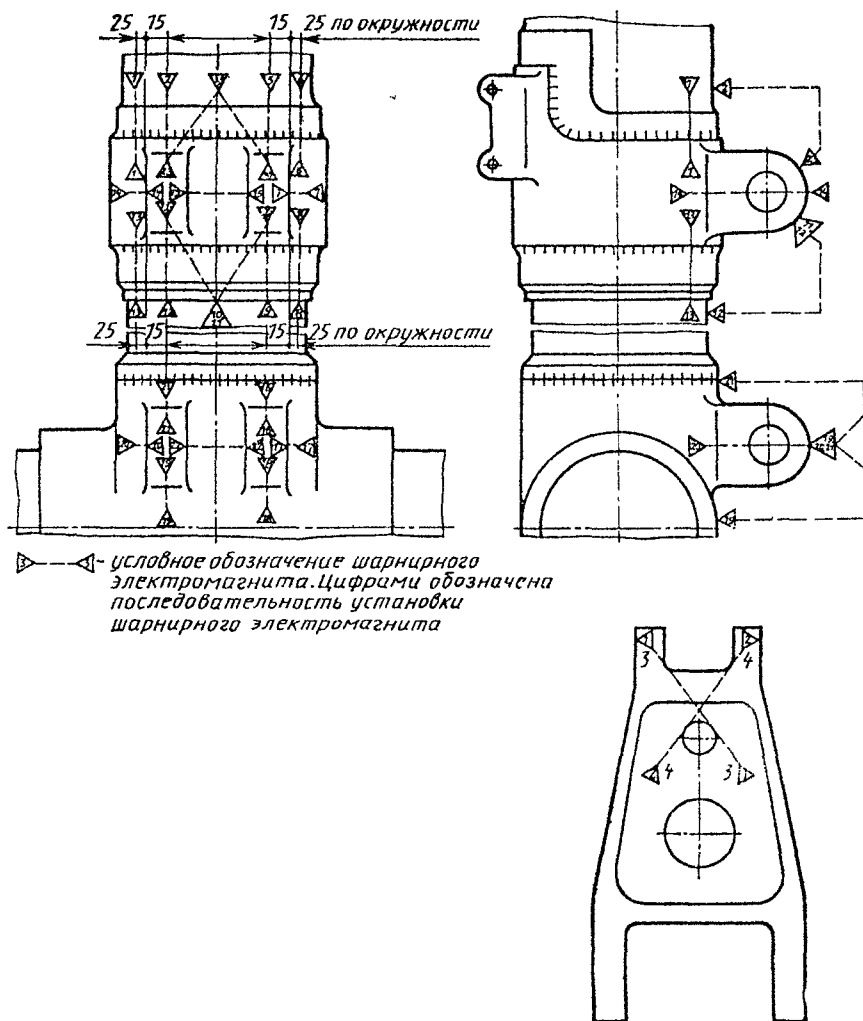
Схема установки шарнирного электромагнита на цилиндре, штоке и нижнем звене шлиц-шарнира основной опоры 24-4101-0А
